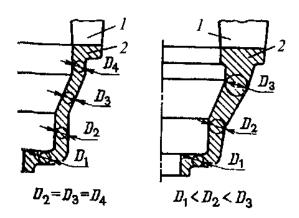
Конструкции литых деталей, обеспечивающих одновременное (a) и направленное (б) затвердевание отливок: 1 - прибыль; 2 — отливка
